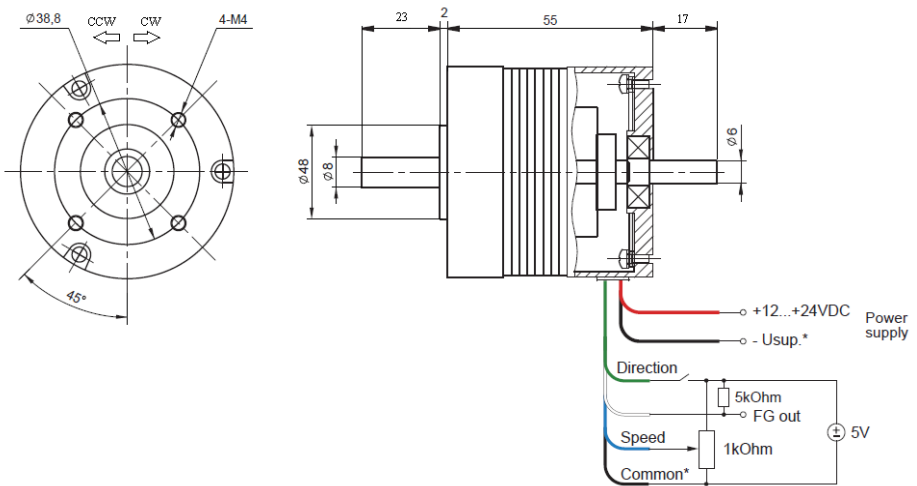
Схема подключения, габаритные и присоединительные размеры привода
